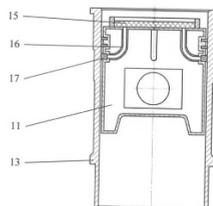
схема смазывания рабочей поверхности трения гильзы цилиндра.
